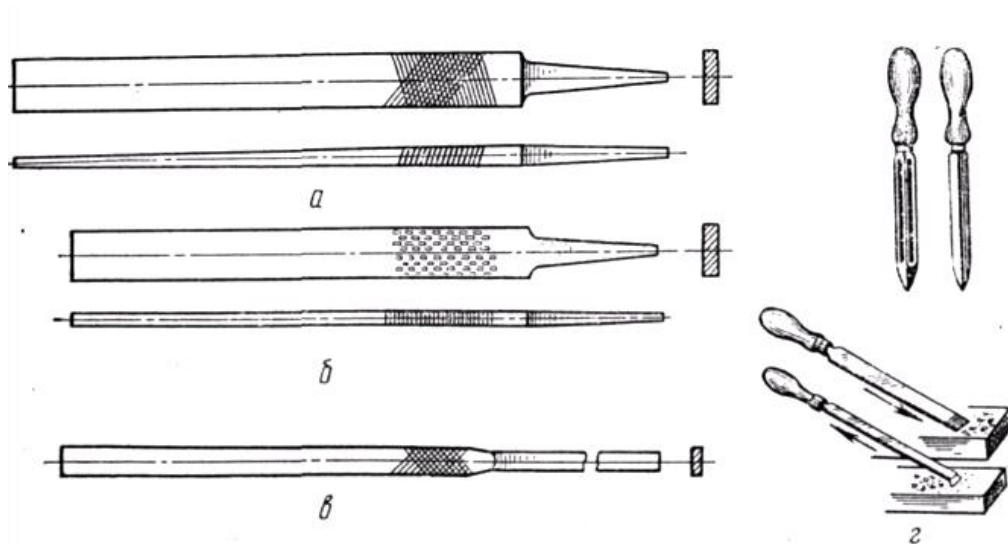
Інструменти для обпилювання і шабровки:
